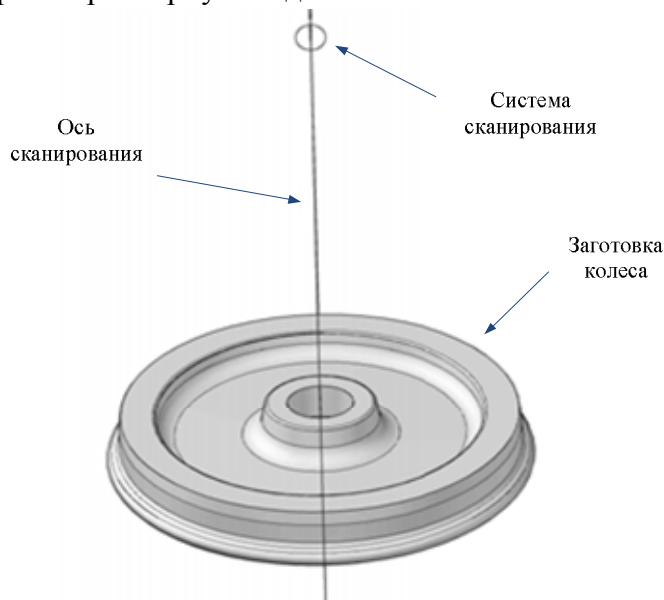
Трехмерная модель относительного расположения поверхности измерительной системы и заготовки колеса
